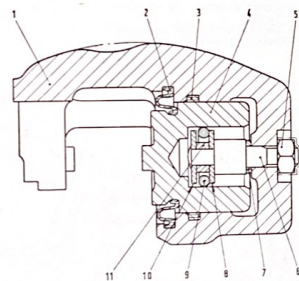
COUPE. Sección en el mecanismo de freno delantero.
